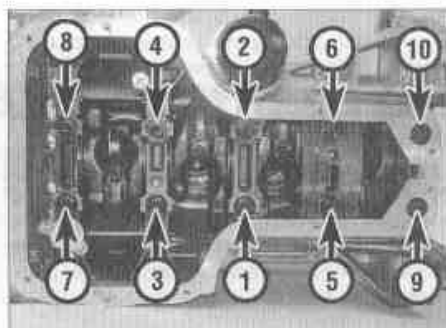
Последовательность затяжки болтов корпуса коренных подшипников (показан бензиновый двигатель)
